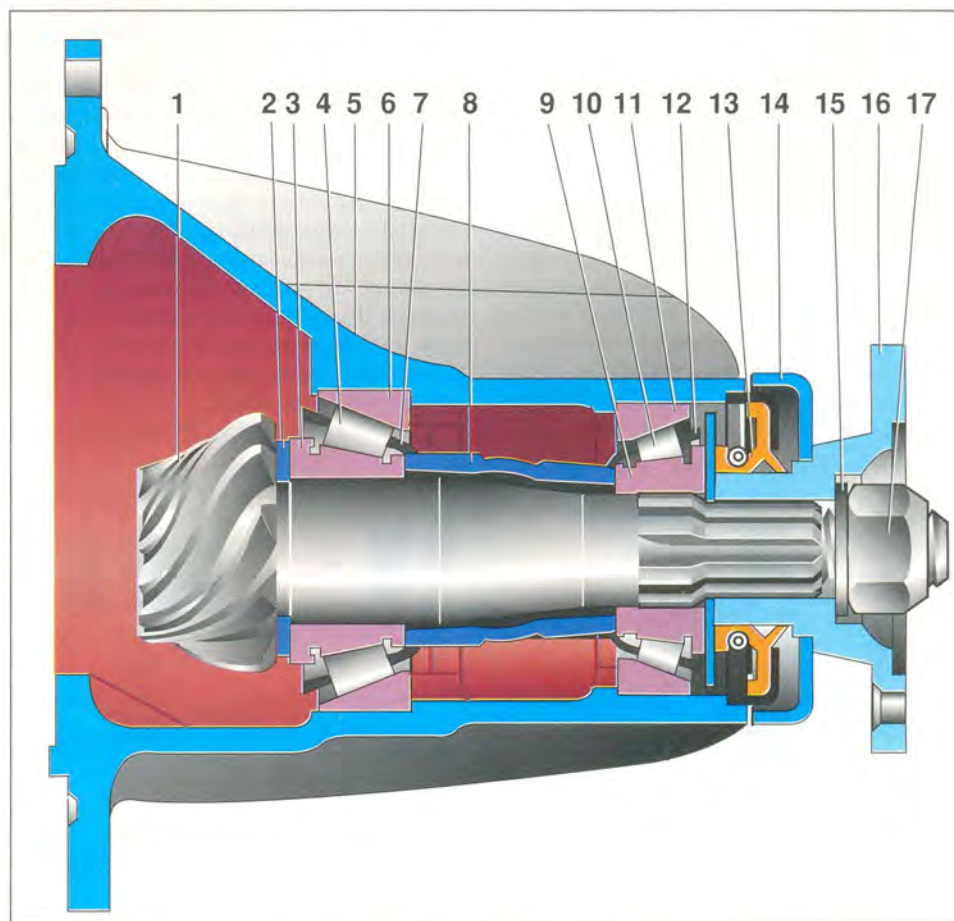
Установка ведущей шестерни редуктора: 1 – ведущая шестерня; 2, 15 – шайба; 3, 9 – внутреннее кольцо подшипника; 5 – корпус; 6, 11 – наружное кольцо подшипника; 7, 12 – сепаратор; 8 – распорная втулка; 13 – сальник хвостовика; 14 – грязеотражатель; 16 – фланец хвостовика; 17 – гайка.
